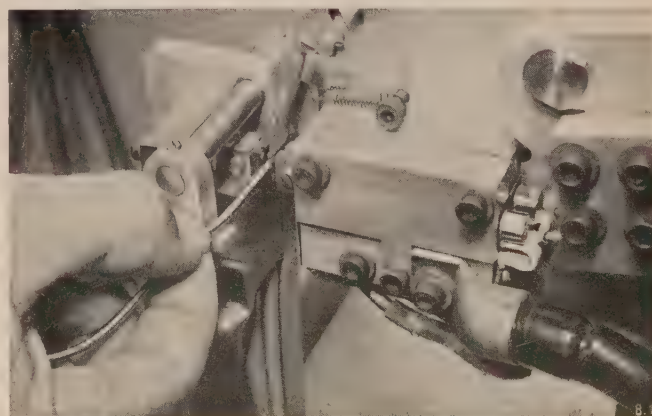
Widerstands-Schweißmaschine zum Anschließen der Wendeln von Rohrheizkörpern.
